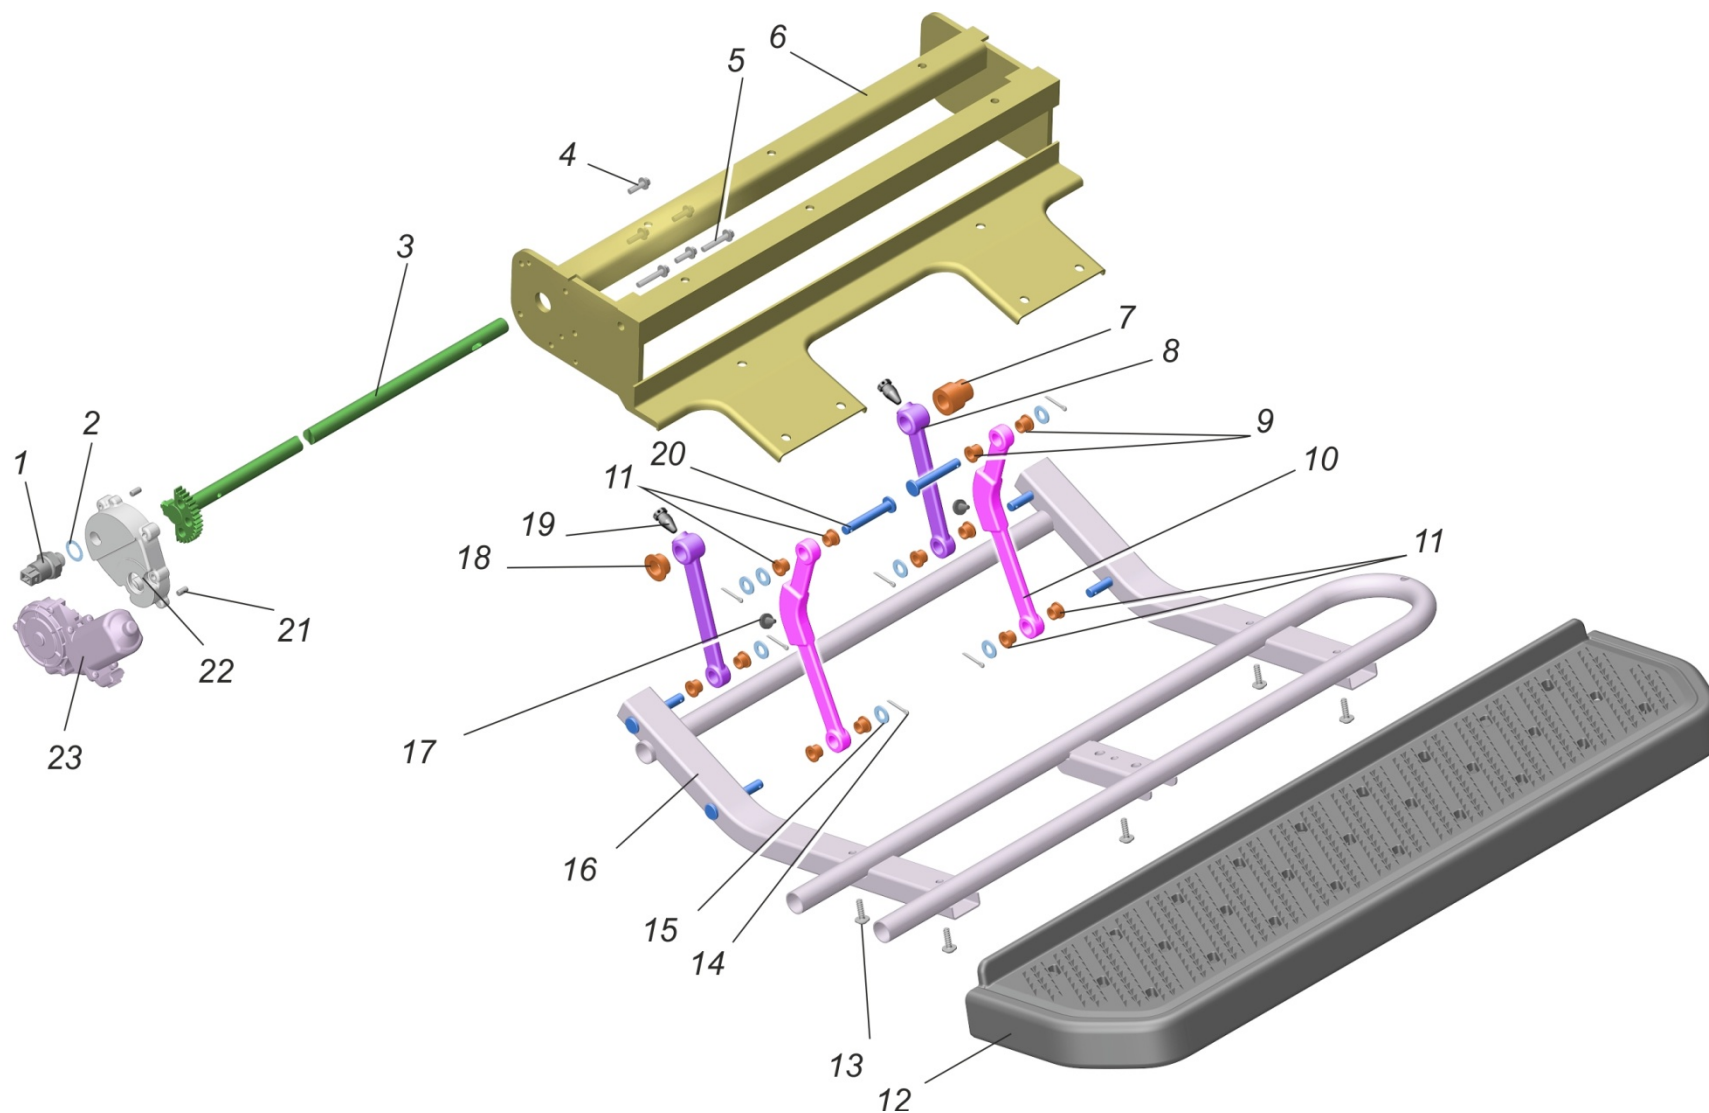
Выдвижная подножка: 1 – датчик убранного положения подножки; 2,15 – шайбы; 3 - вал ведущий в сборе с шестерней; 4- болт разблокировки; 5– болт; 6 - каркас; 7 – втулка дистанционная; 8,10 - рычаги; - 9,11 - втулки; 12 – подножка дополнительная; 13, 19 – винты; 14 – шплинт; 16 - балка подножки с осями; 17 – буфер; 18 - втулка опорная вала; 20 – ось; 21 - штифт; 22 – корпус; 23 – моторредуктор
